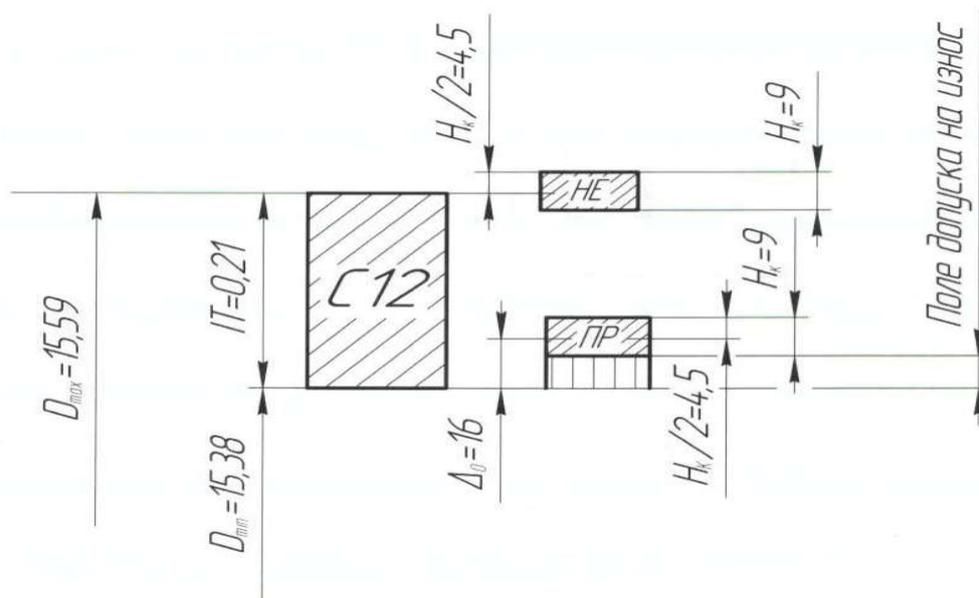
Схема расположения полей допусков калибр – пробки для отверстия диаметром
